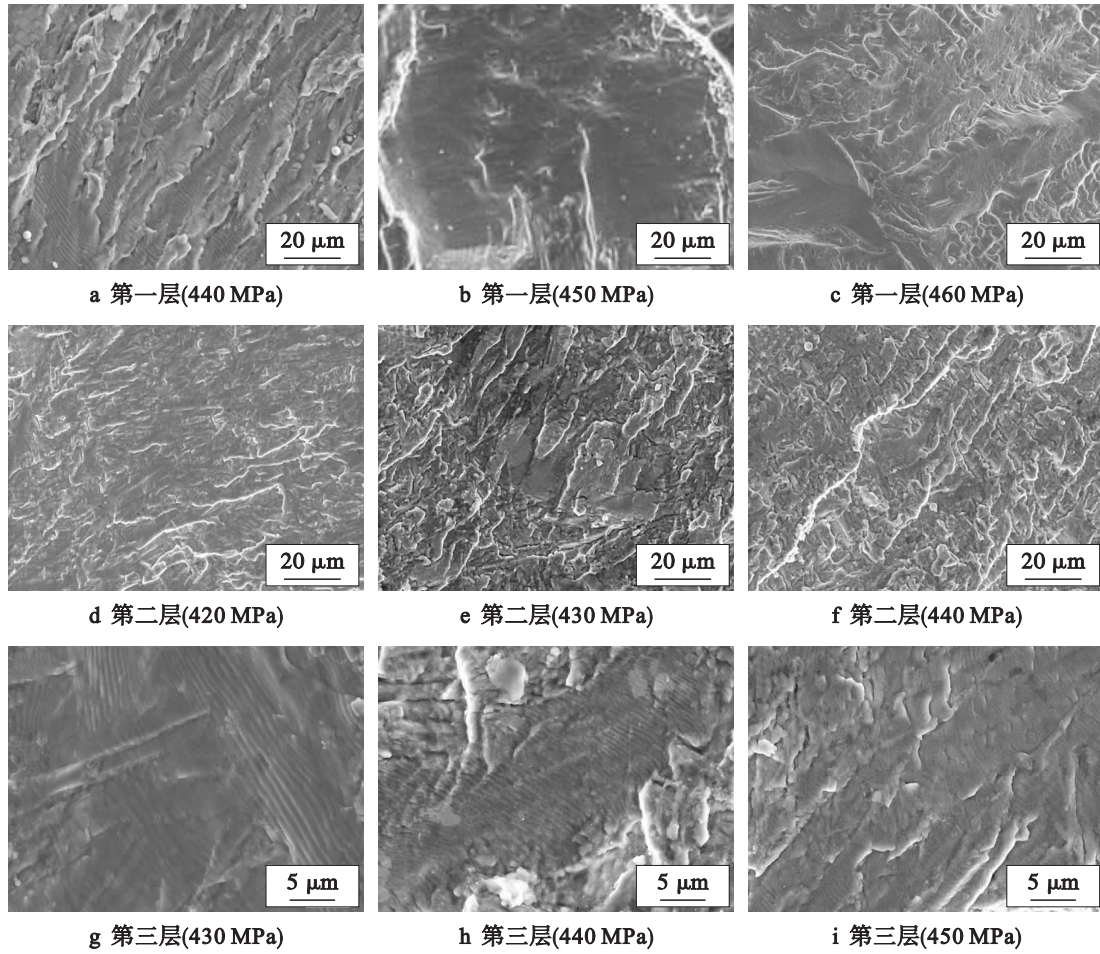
焊接接头在不同应力下的高周疲劳裂纹扩展区形貌
